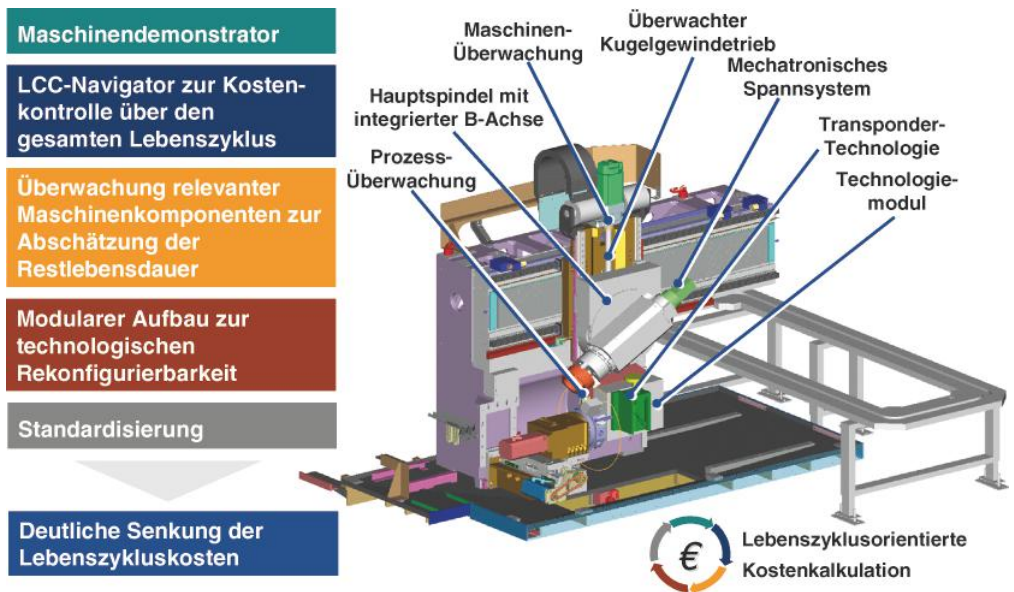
Projektziele und Aufbau des Maschinendemonstrators
